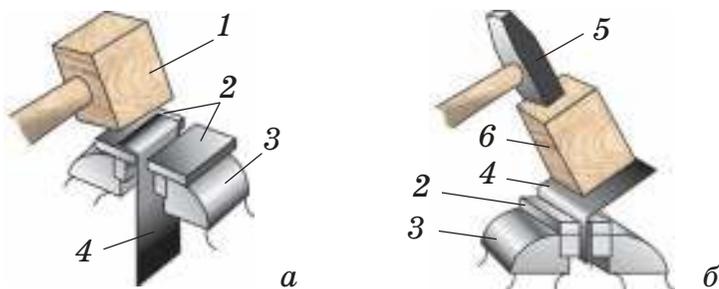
Гибка тонколистового металла в слесарных тисках:
